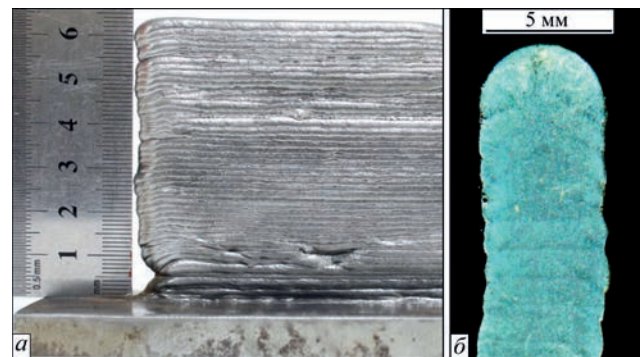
Наплавлений PAW-CW способом зразок зі сталі 09Г2С (G3Si1): а – загальний вигляд бокової поверхні; б – поперечний макрошліф
